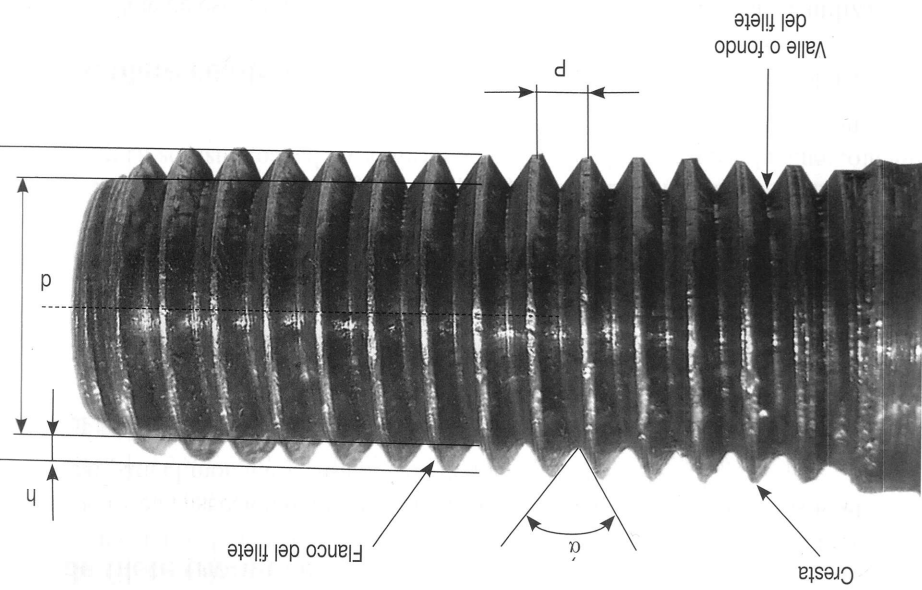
A. Principales dimensiones de la rosca de un tornillo.
